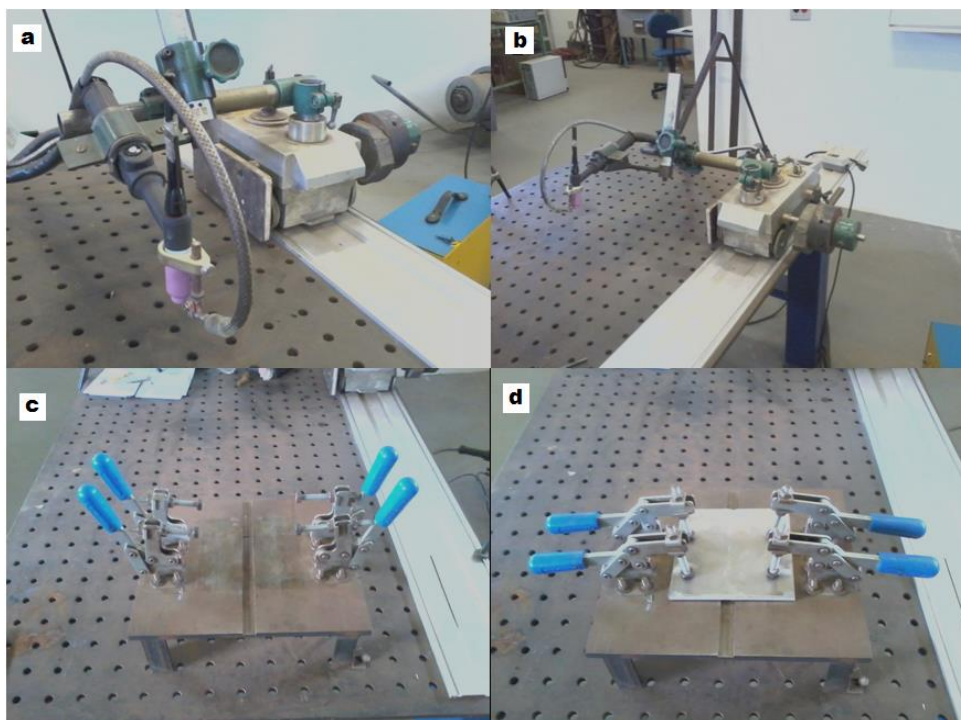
(a) e (b) Tocha de soldagem acoplada ao carro sobre trilhos, 9 (c) e (d) grampo de pressão utilizado para fixar os corpos-de-prova.
